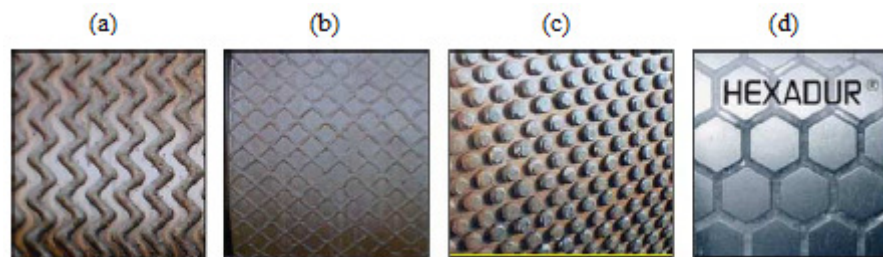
Superficies de revestimientos para rodillos: (a) welded, (b) chevron, (c) studded y (d) HEXADUR. (de Daniel et al., 2004)
